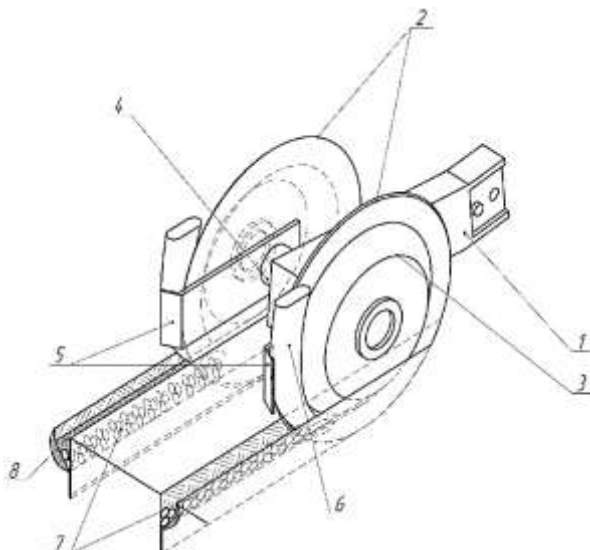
Технологическая схема двухдискового сошника с внешними симметричными усеченно-конусными ребрами и нулевым углом атаки дисков: 1 – корпус; 2 – диски; 3 – ребра; 4 – ось; 5 – пластины; 6 – семянаправитель; 7 – семена; 8 – бороздка
